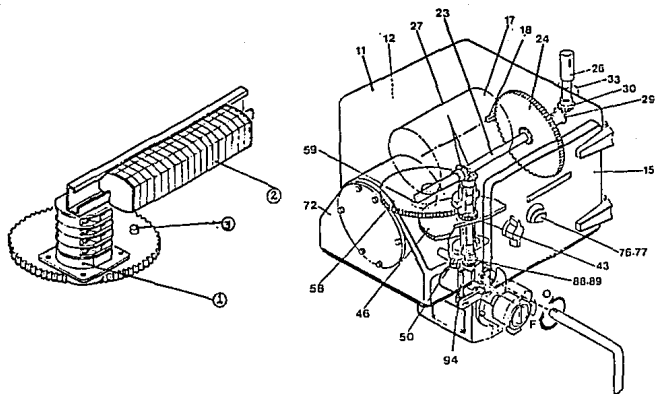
(Derecha) Mecanismo de transmisión y engranaje del equipo de mando, (izquierda) - componentes del interlock.
